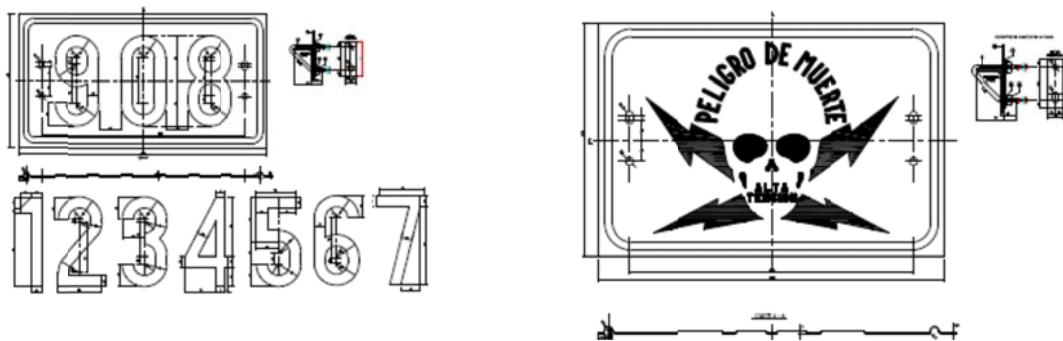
Accesorios que se colocaran en cada torre de transmisión
